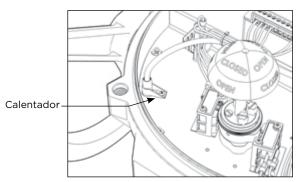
Calentador Instalado en una Placa de Sensores de S70.
